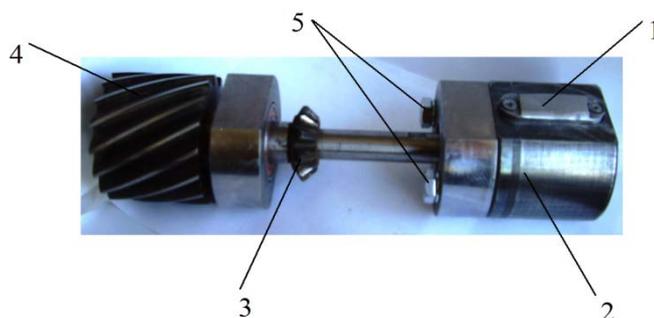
Калибровально-термопротяжный узел: 1 – термопротяжная пластина; 2 – противовес; 3 – шестерня зубчатой конической передачи; 4 – фреза для снятия припуска; 5 – фиксирующие болты
